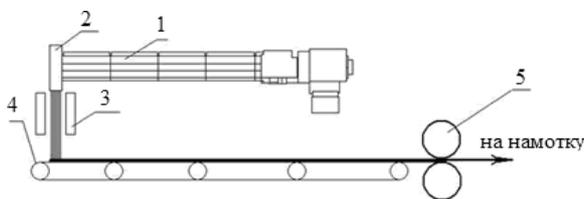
Структурная схема установки для изготовления фильтрующего материала из полипропилена: 1 – экструдер; 2 – формующая головка; 3 – фильера; 4 – конвейер; 5 – барабаны
